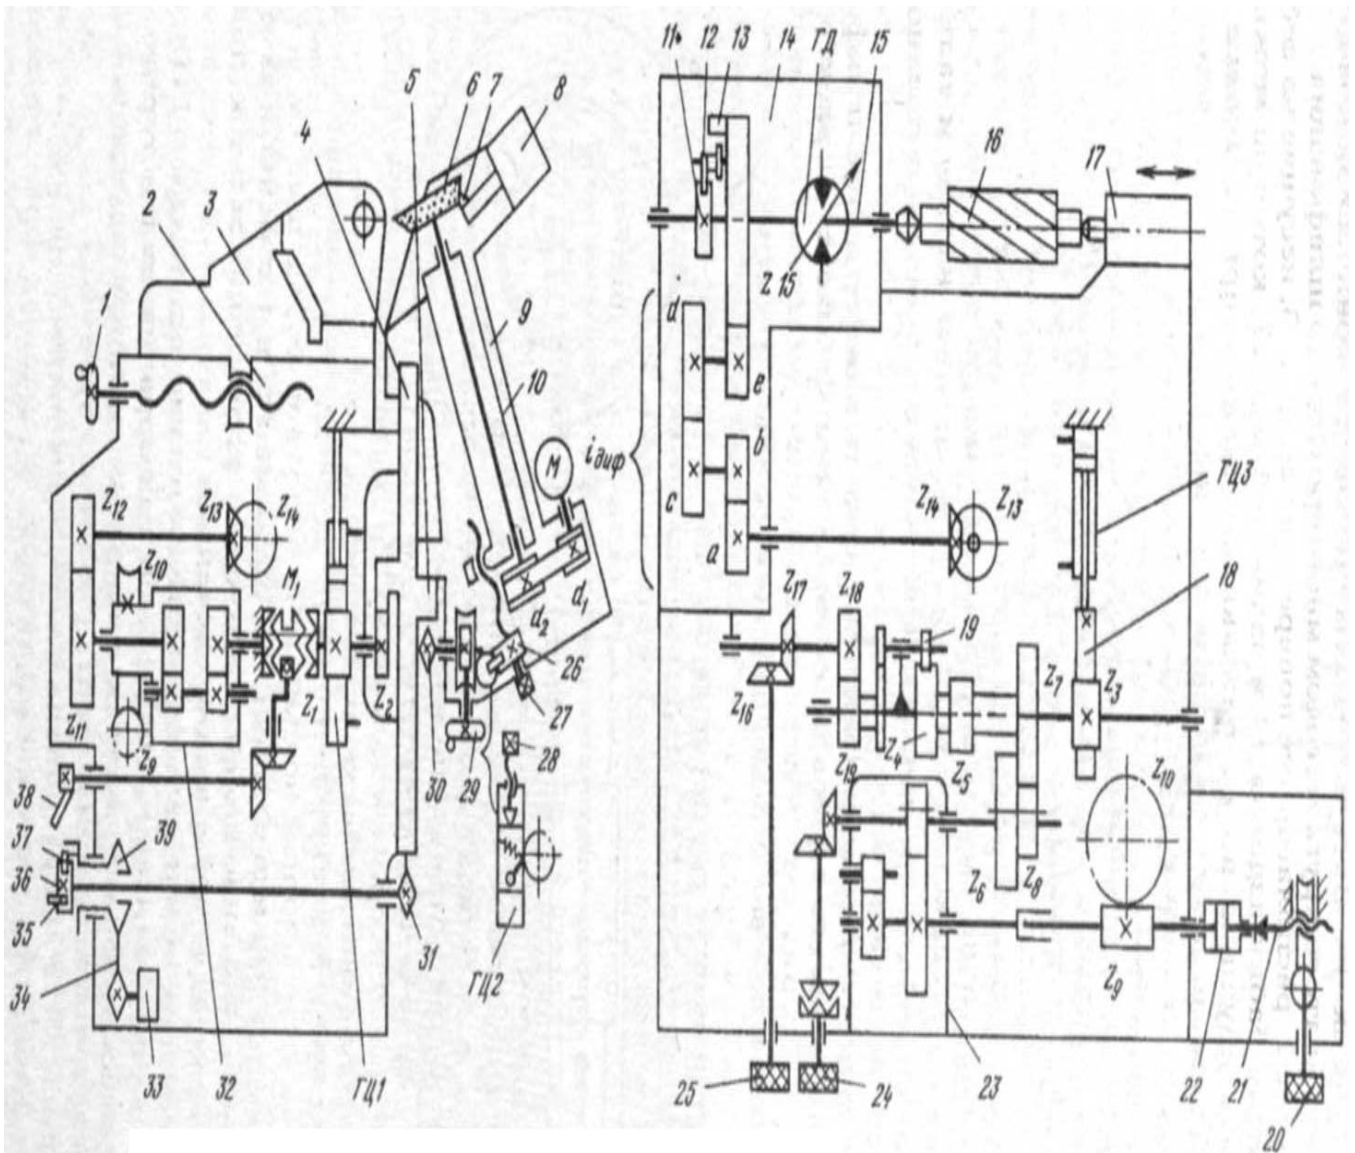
Кинематическая схема заточного полуавтомата модели 3А662 для заточки червячных зуборезных фрез.
